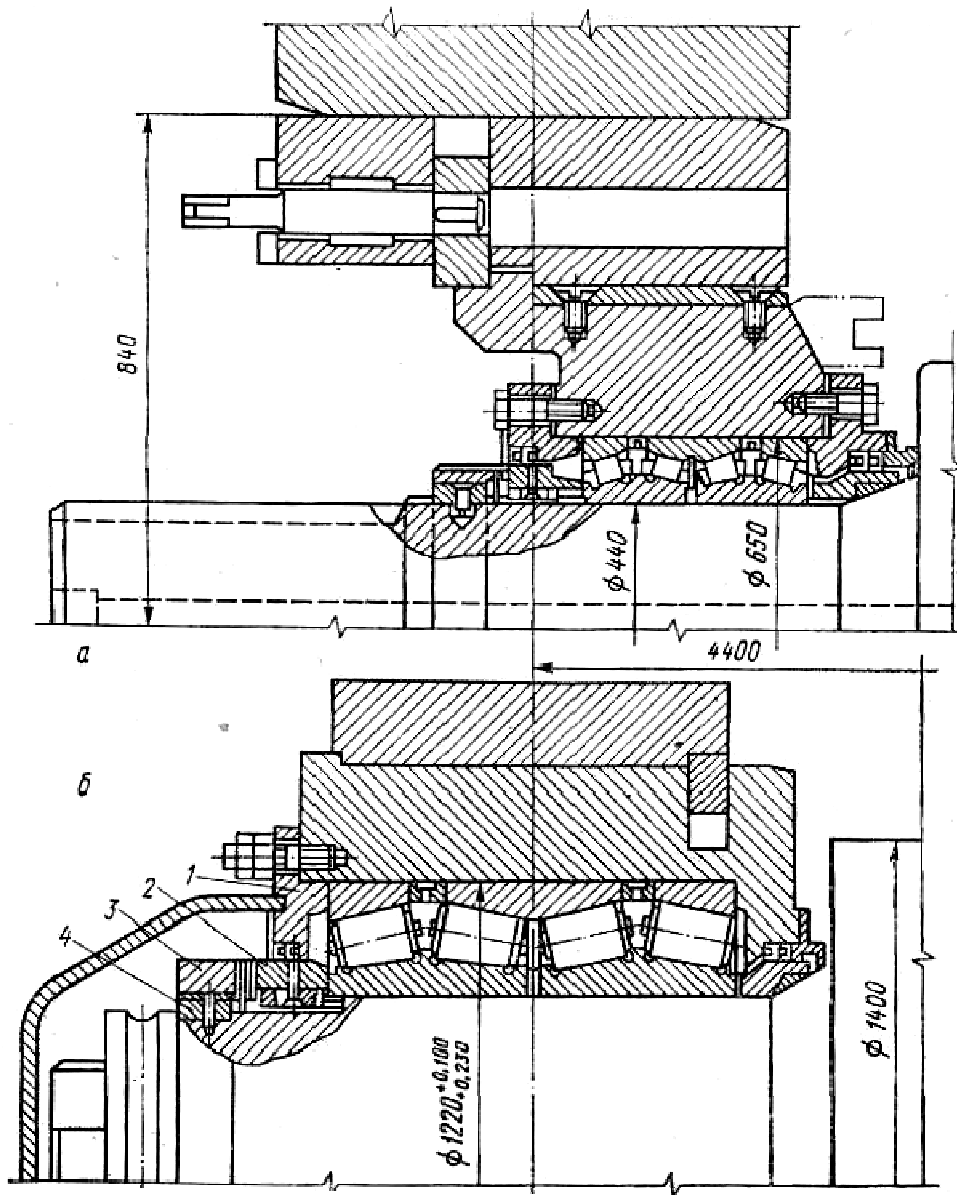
Установка рабочего (а) і опорного (б) валків чотирьох валкового стана 2800 на роликівих конічних підшипниках
